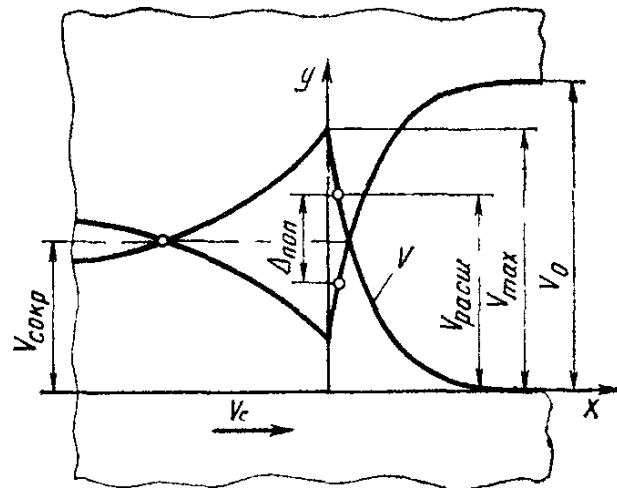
Схема образования поперечной усадки при односторонней стыковой сварке:
